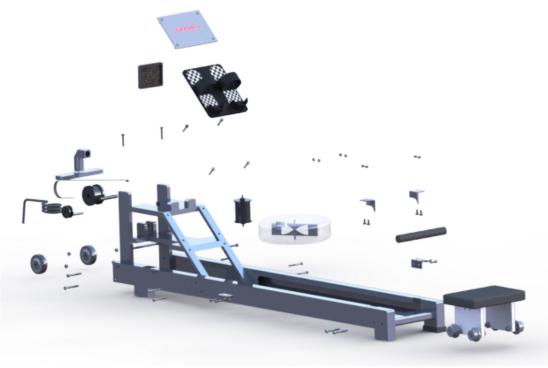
Vista explotada de la remadora completa y cada una de sus partes.
